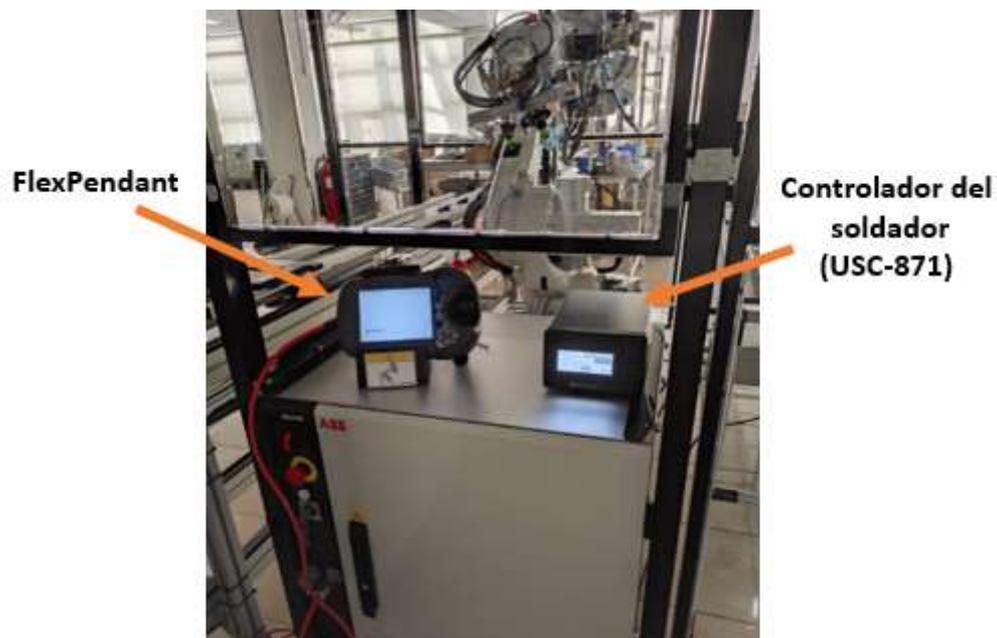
Fotografía del FlexPendant y controlador del soldador.
